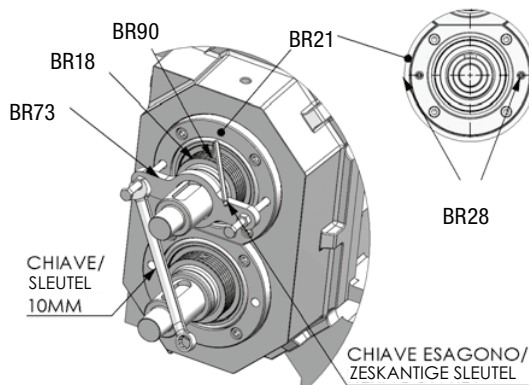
Montage mechanische dichtingen (fase 2).
